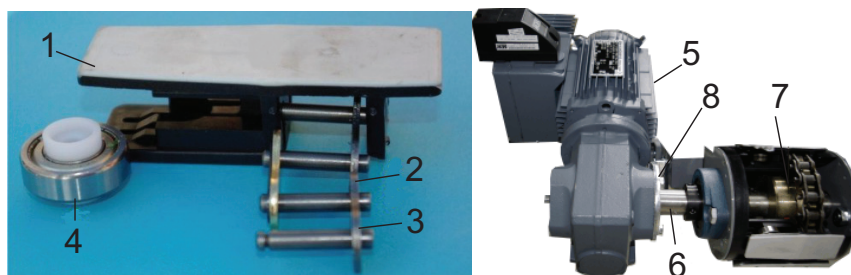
Composants de la chaîne du convoyeur, de l'extrémité d'entraînement du convoyeur et du moteur à engrenages
